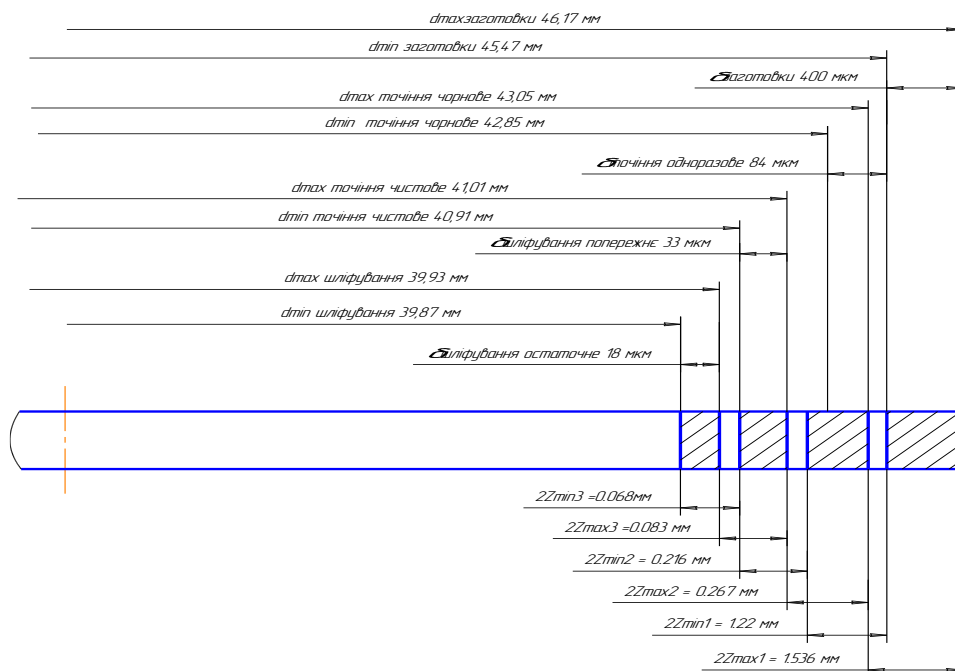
Схема графічного розташування полів допусків деталі
